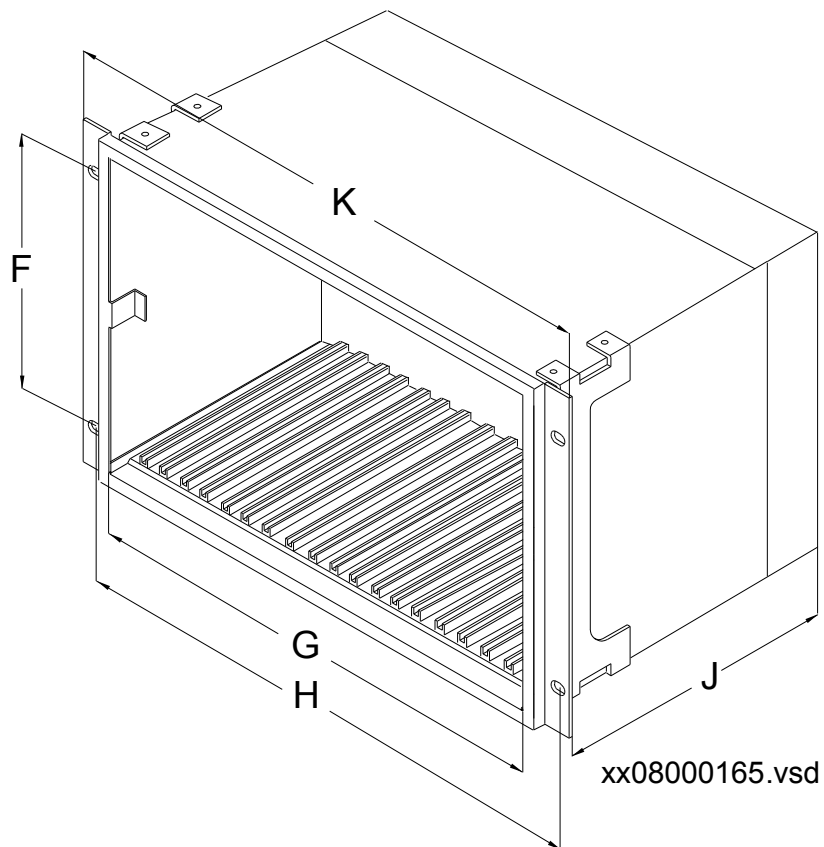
Корпус с задней крышкой и комплектом для монтажа в 19-дюймовой стойке
